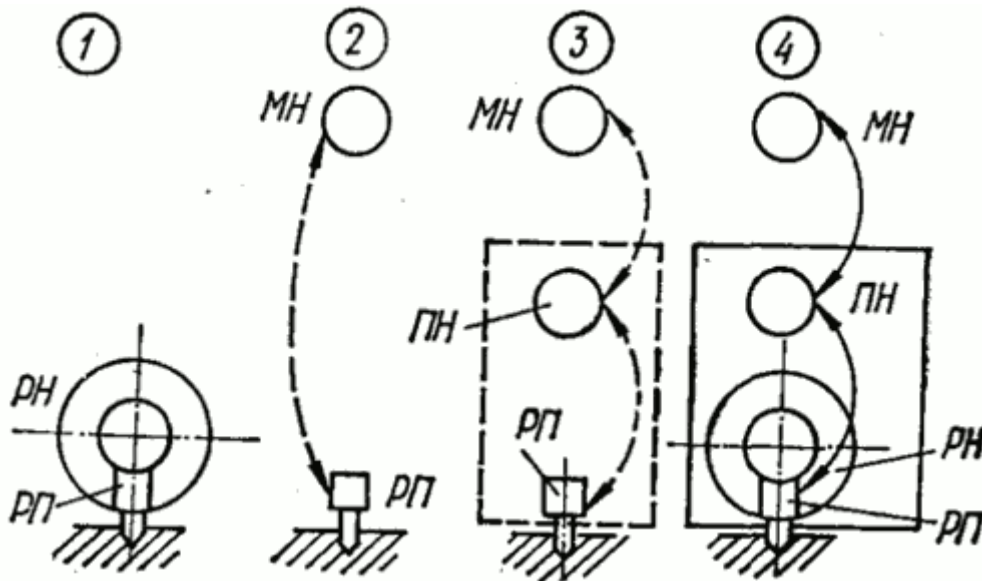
Типи пристроїв автоматичної зміни інструменту: МН - магазинний накопичувач; ПН - проміжний накопичувач; РН - робочий накопичувач (багато інструментальних головок); РП - робоча позиція
